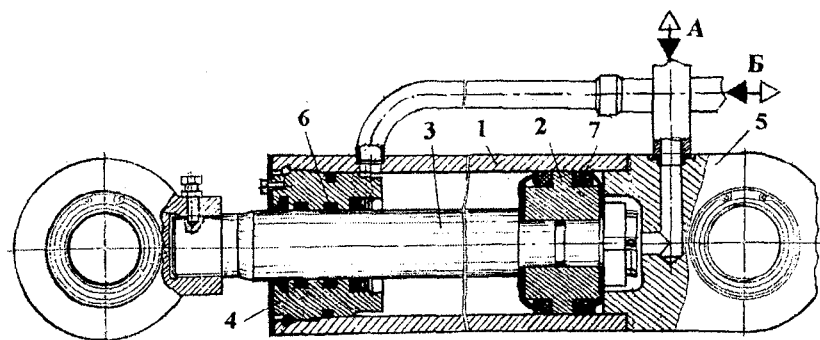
Конструктивное исполнение одноштокового двухходового гидроцилиндра
